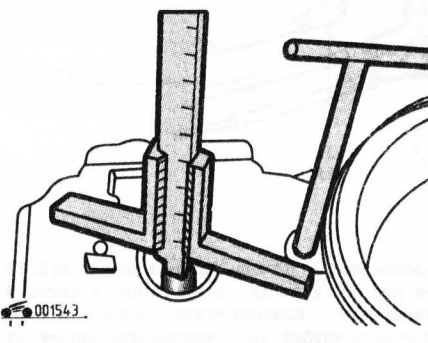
Регулировка основной установки регулировочного рычага измерителя потока воздуха
